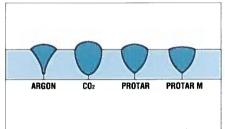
Efecto de la composición del gas de protección sobre el perfil soldado o forma de la costura.
